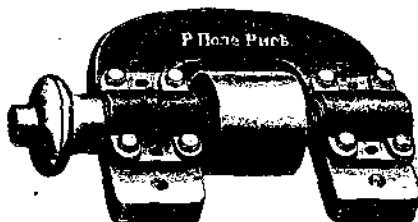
Вал для круглой пилы со шкивом между подшипниками.
